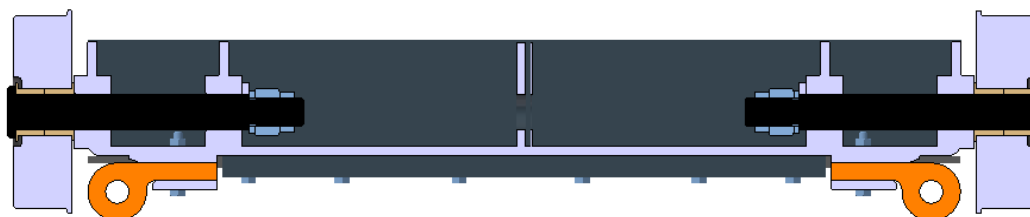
Conjunto sistema rodillos compuerta canal.
